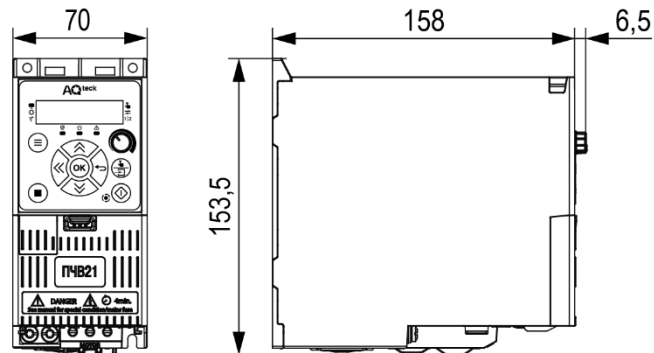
Габаритні розміри ПЧВ у корпусі 3
